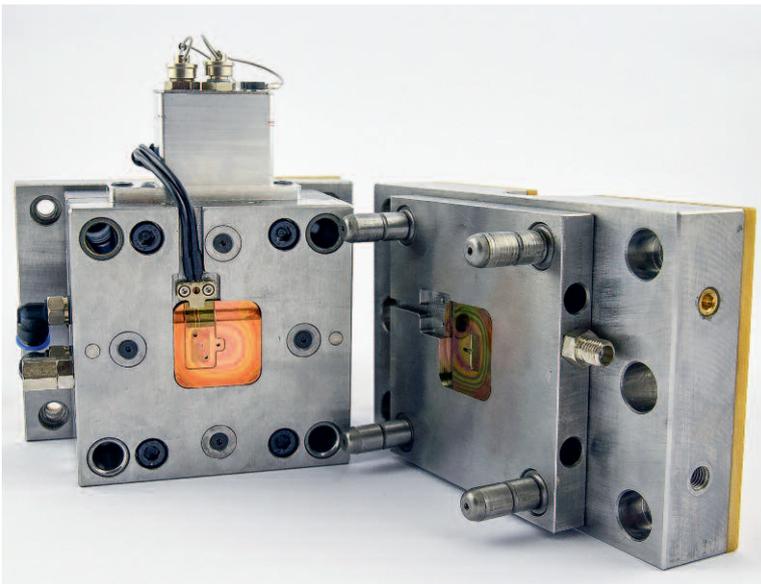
Mikrospritzgusswerkzeug mit kontaktierter Heizschicht auf der Auswerferseite
